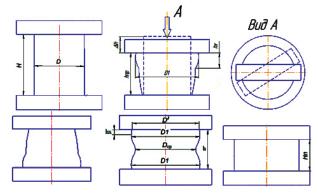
Схема осадки цилиндрической заготовки с предварительным профилированием разгонкой узким бойком
